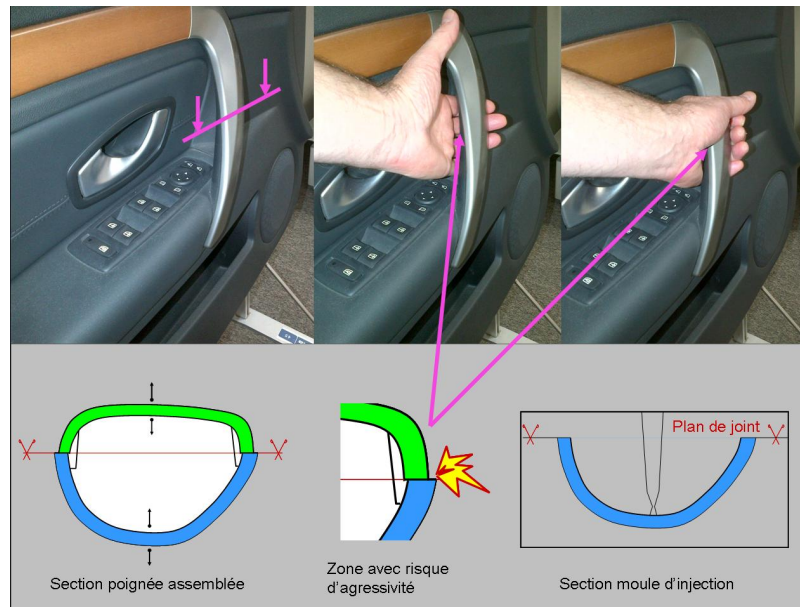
Exemple d'un risque d'agressivité causé par le plan de joint
